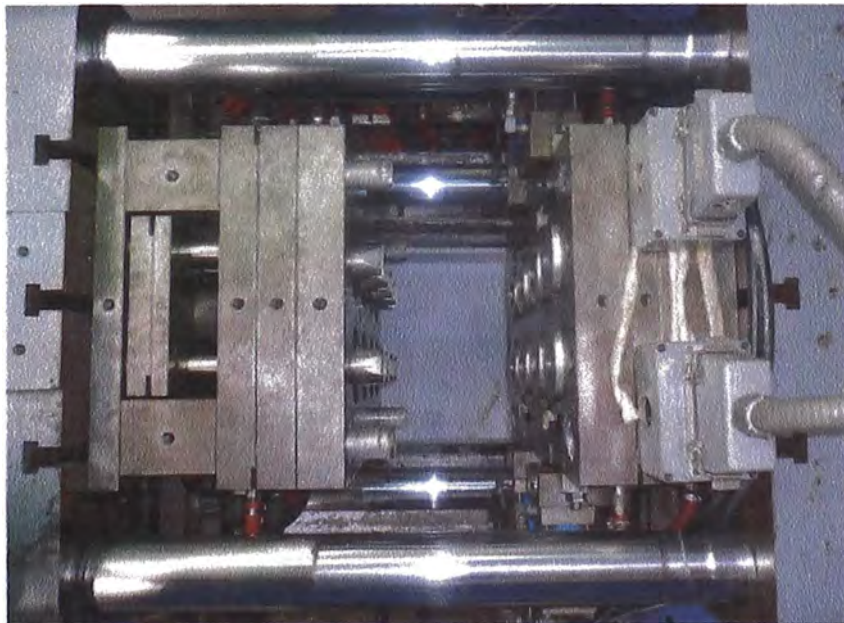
Montaje de molde base en la inyectora F-C-S HT250i
